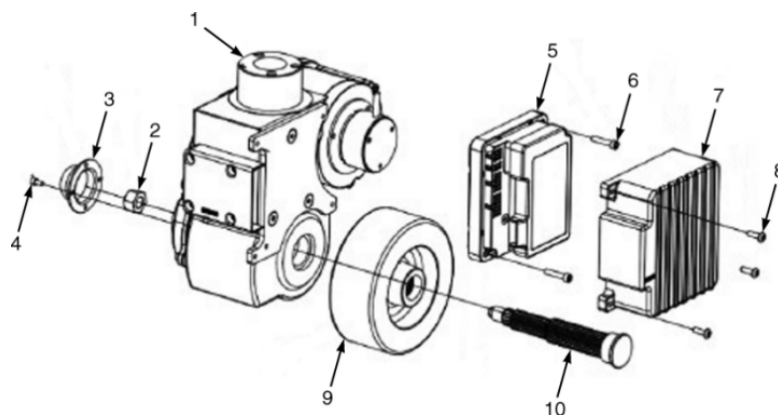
Vue éclatée de l'ensemble de la roue motrice.
